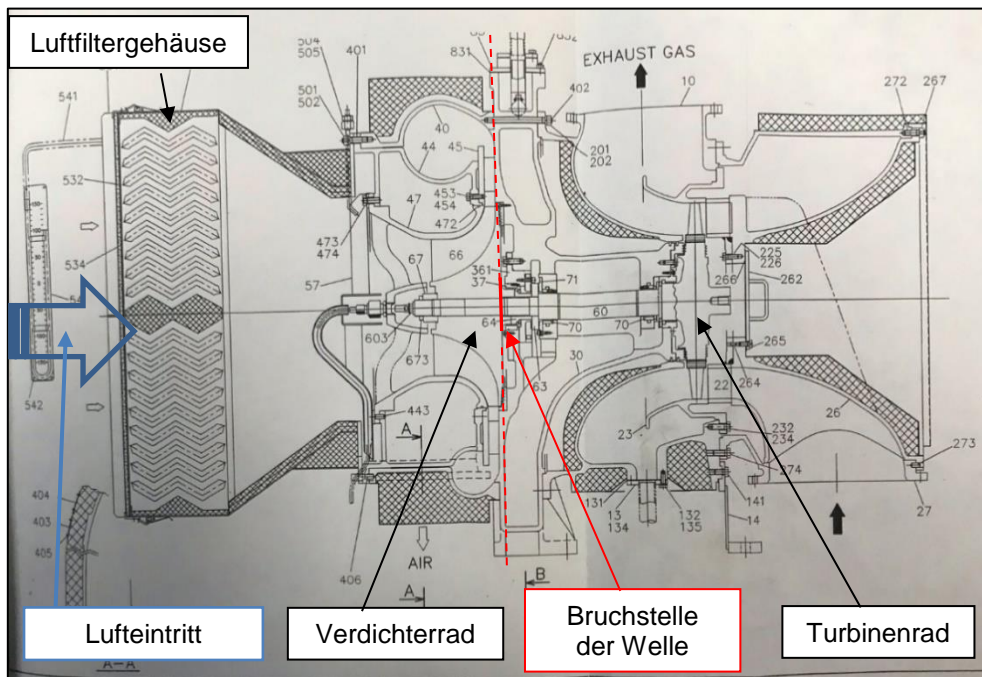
Technische Zeichnung des Turboladers<sup>9</sup>
